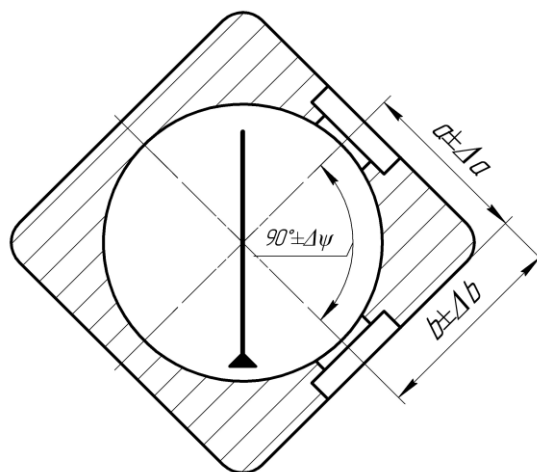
Погрешность, обусловленная неточностью изготовления корпуса
